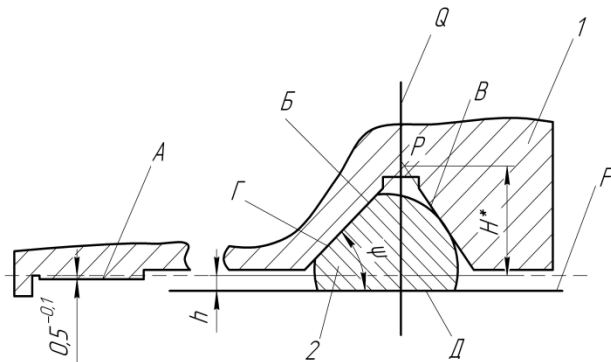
Схема расположения «скрытых баз» по новой схеме простановки размеров:
